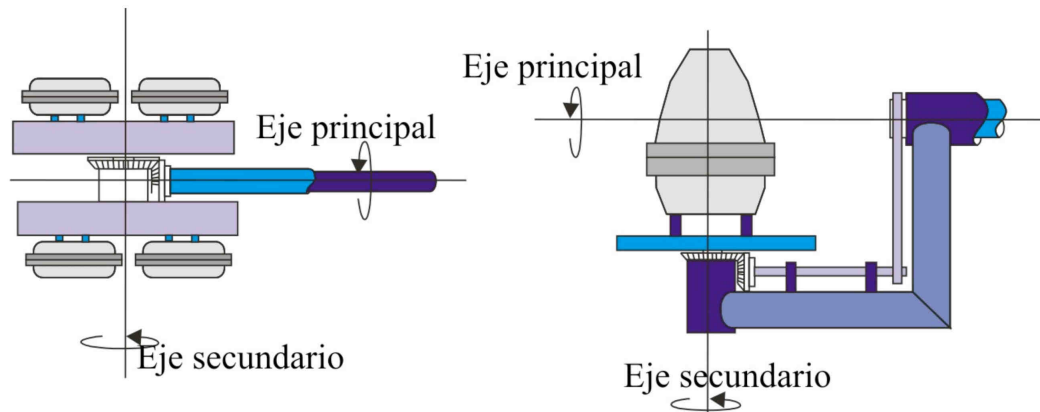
Máquinas de moldeo rotacional de brazo recto y acodado para giros completos en dos ejes.
